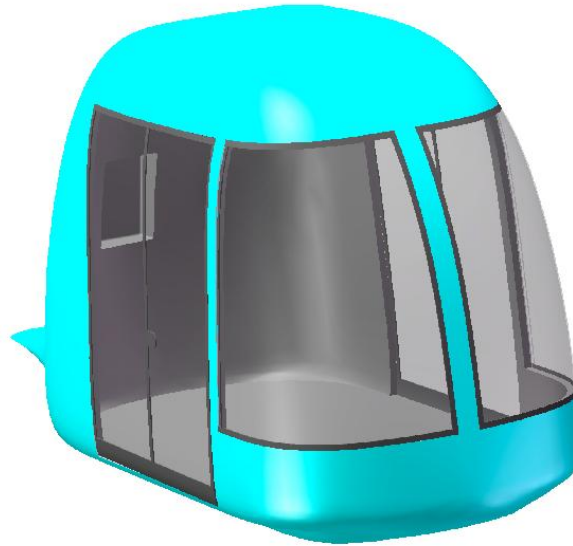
Корпус юнибуса Ю-324П исполнения 01
